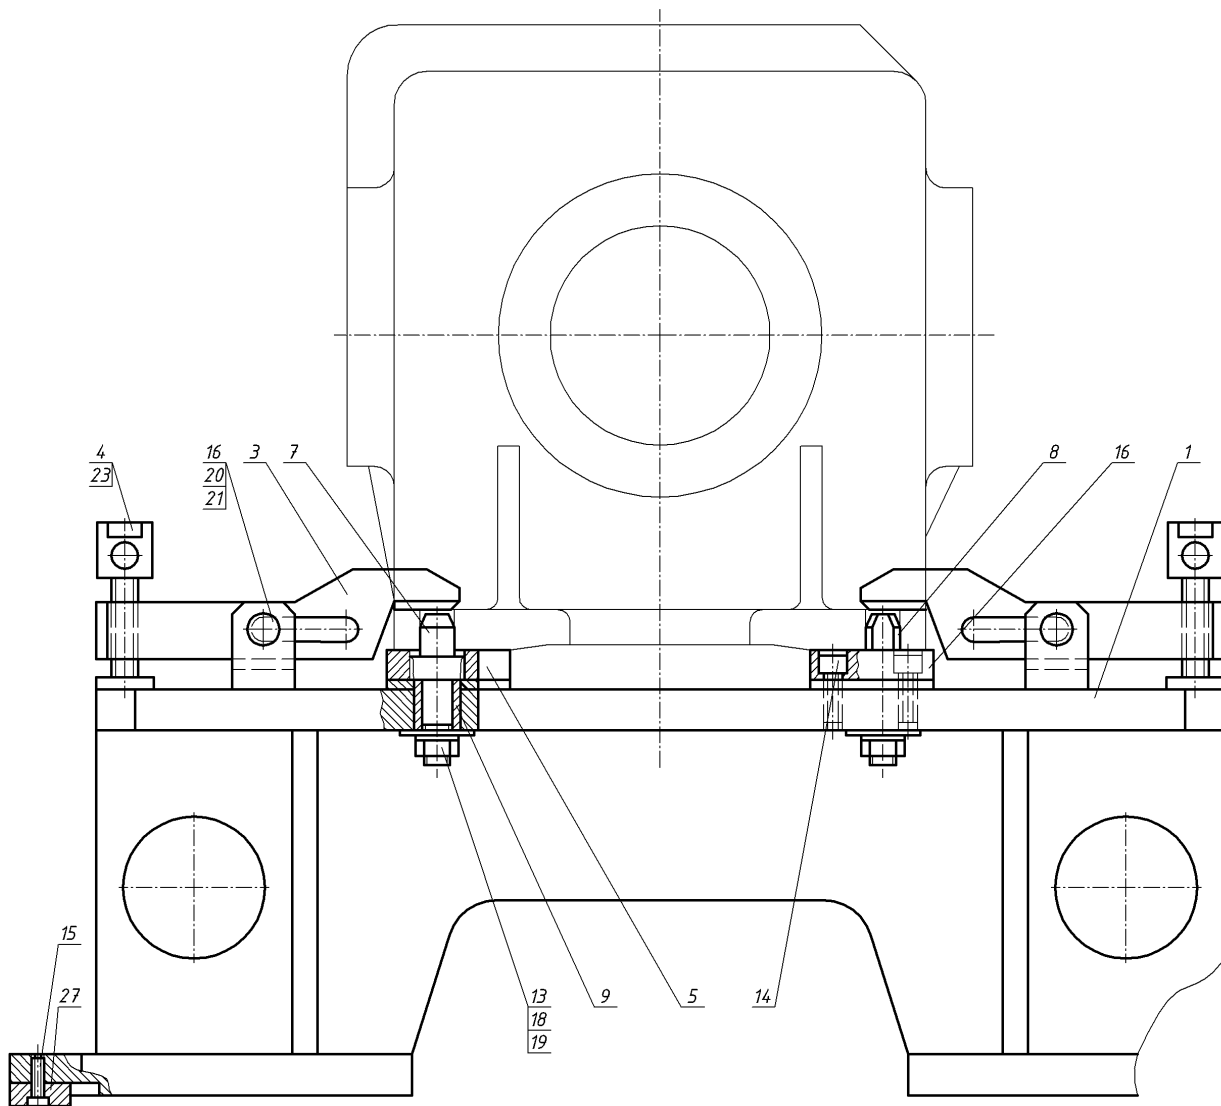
Пристрій для фрезерування та розточування отворів
